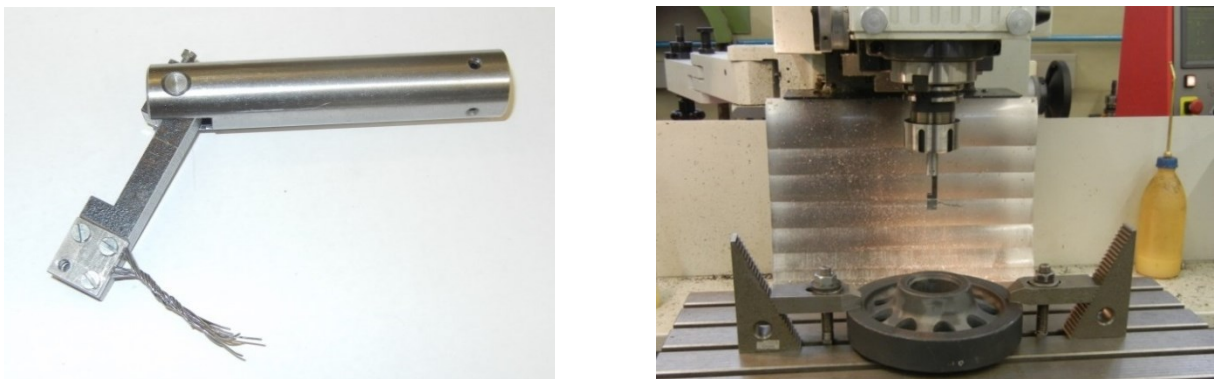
Fliehkräftauslenkungswerkzeug mit Stahlborsten (links); Werkzeug eingespannt in Frässpindel und Werkstück auf Fräsmaschinentisch aufgespannt
